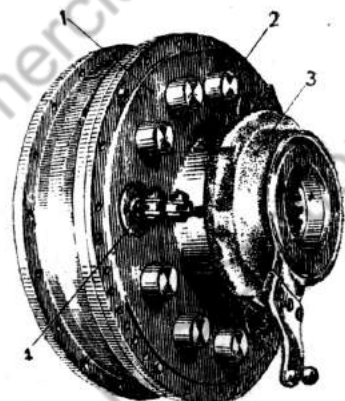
Главный фрикцион (общий вид со стороны двигателя): 1 — несущий диск; 2 — стакан; 3 — подвижная чашка выключенная; 4 — натяжной рычаг
